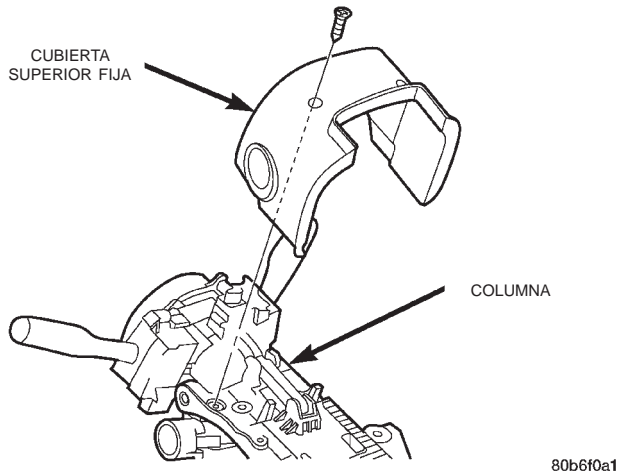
Desmontaje e instalación de cubierta fija de la columna
